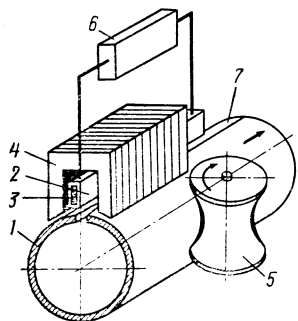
Сварка труб со стержневым индуктором:
